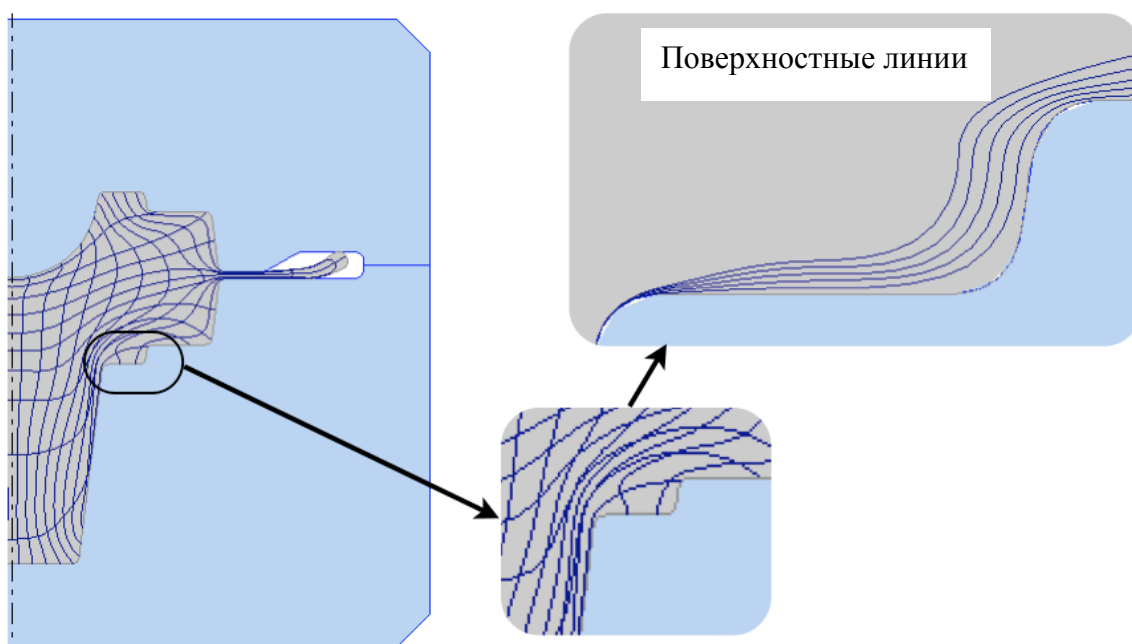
Линии Лагранжа при облойной штамповке заготовки с $H/D=2,5$
